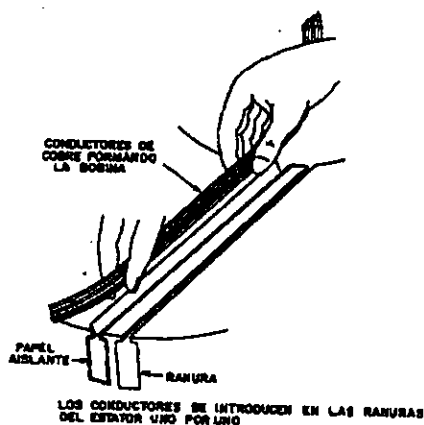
Forma en que se colocan las bobinas prefabricadas dentro de las ranuras del estator de una forma manual. Esta figura fue obtenida del libro de "El ABC De Las Máquinas Eléctricas II (Motores De Corriente Alterna)" de Gilberto Enríquez Harper.
